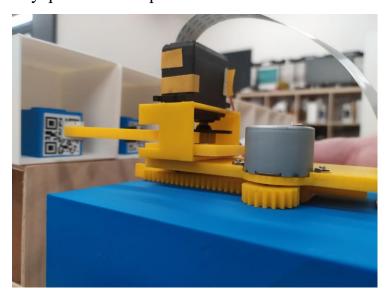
Верхняя зубчатая рейка, внешнее зубчатое колесо, подставка под мотор
